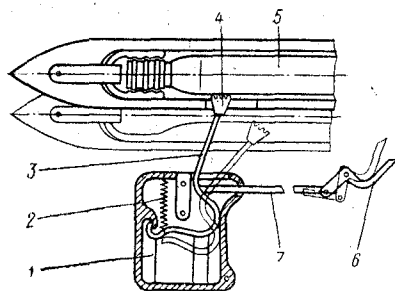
Схема уточного шпуля станка АТ-100-5М
